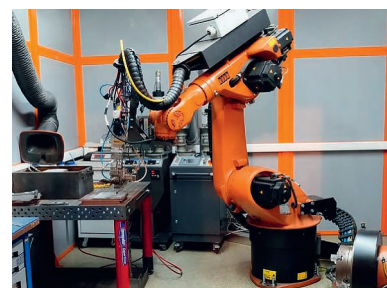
Система лазерной сварки LRS PRO ОКБ «Булат»
